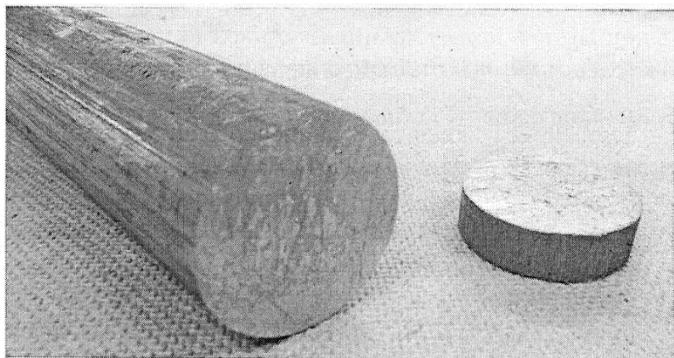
Общий вид прессованного прутка диаметром 57 мм и заготовка для металлографического образца из легированного силумина
